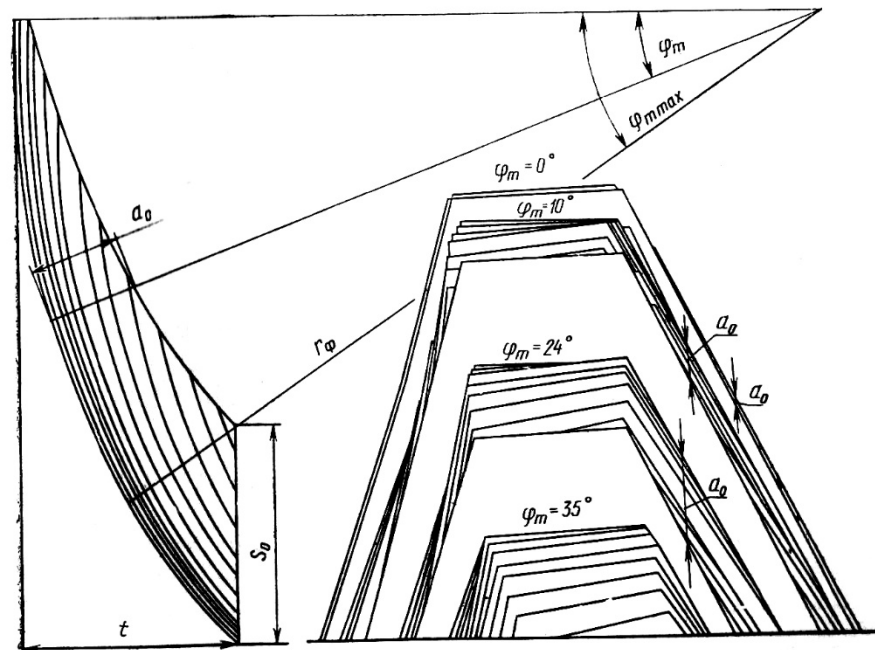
Схема зйому стружок з впадини заготовки зубцями фрези.
